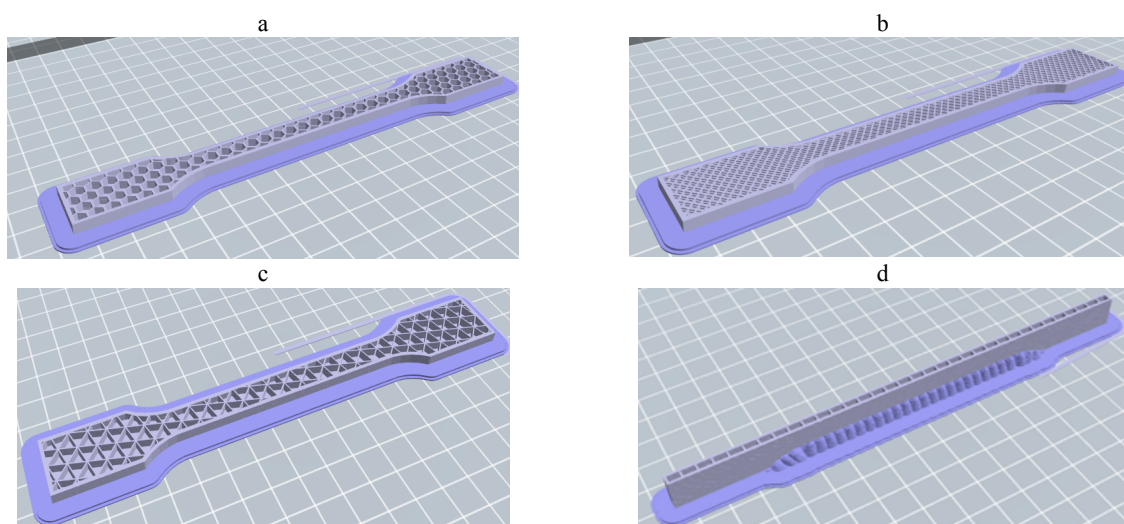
Модели создания образцов с различными формами заполнения: а – шестигранниками (сотами); б – линиями; с – треугольниками; д – печатью линий на ребре
